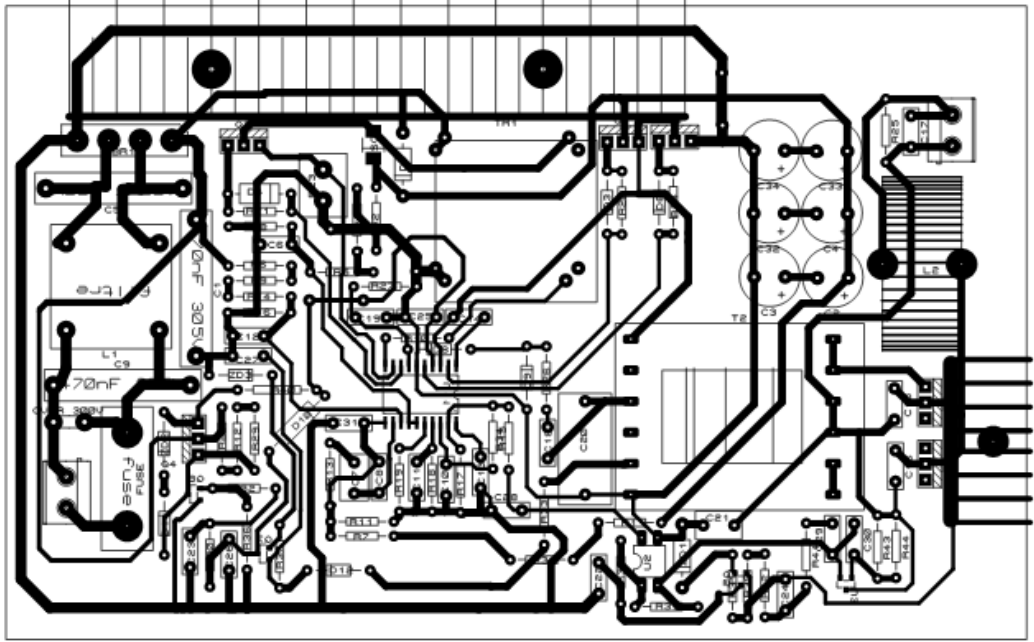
0-30 Volt – 0-3Amper ayarlı güç kaynağı devresi pcb üst görünümü
